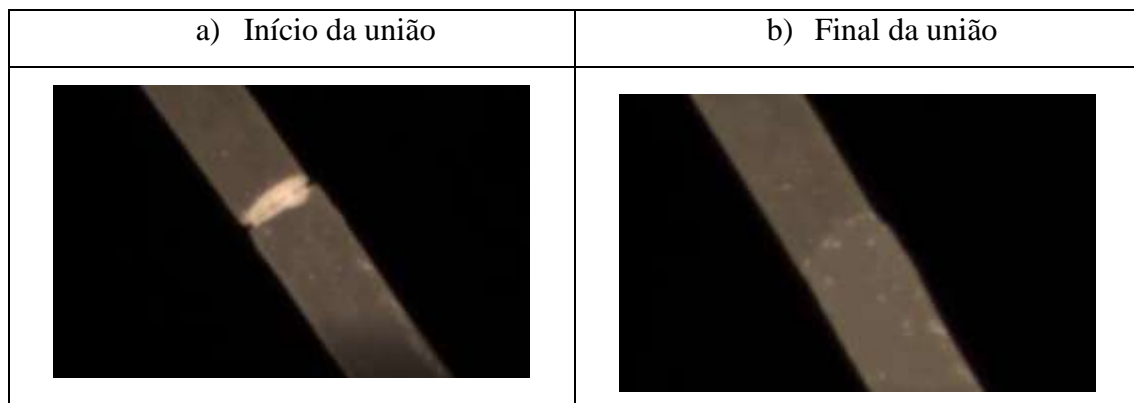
7- Imagens do processo de soldagem dos termopares. (a) início da união e (b) termopar soldado. Fonte: AUTOR, 2020.
